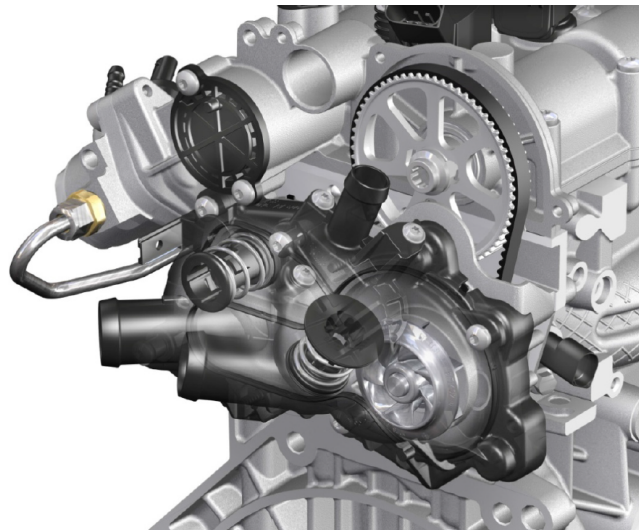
Kühlmittelpumpen-Modul mit integriertem Zweikreisregler [8]
